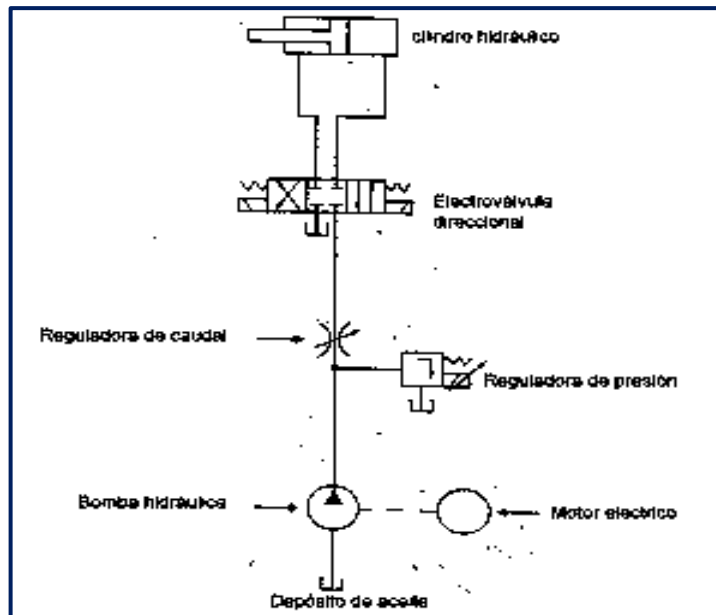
Componentes principales de sistema hidráulico en un equipo de moldeo por inyección.
